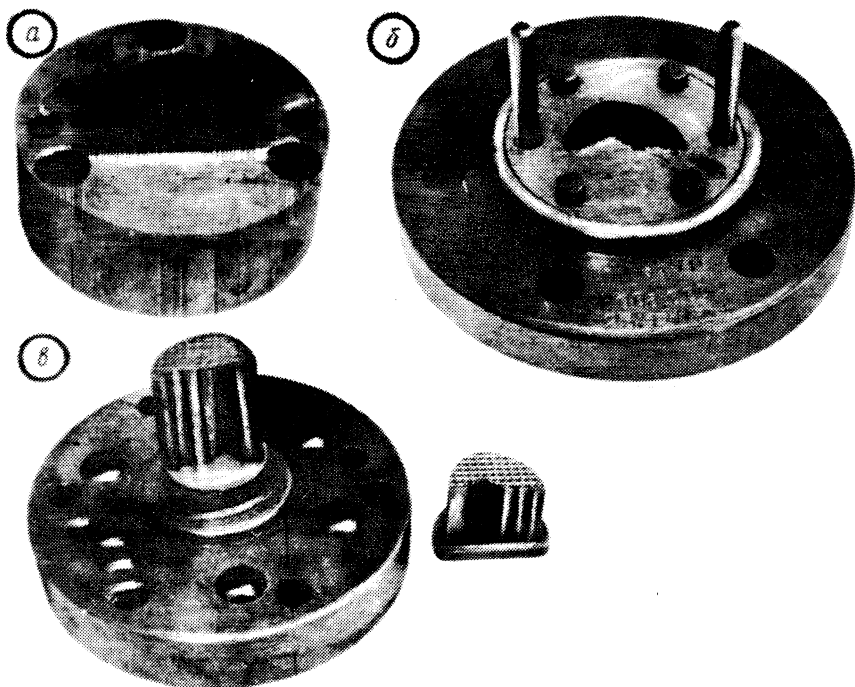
Рабочий инструмент для штамповки пластин КПЕ:
